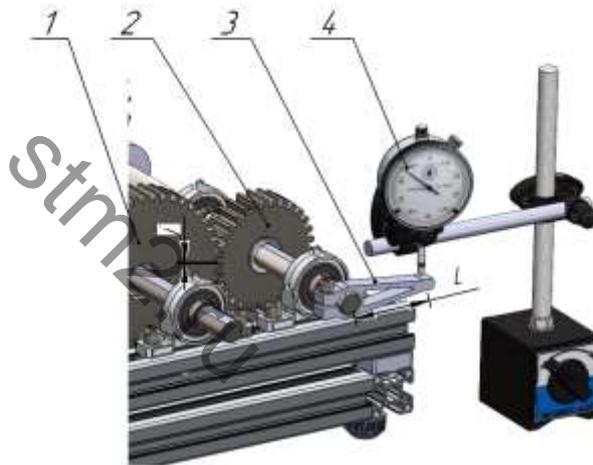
Схема измерения бокового зазора в зубчатом зацеплении с помощью индикатора
